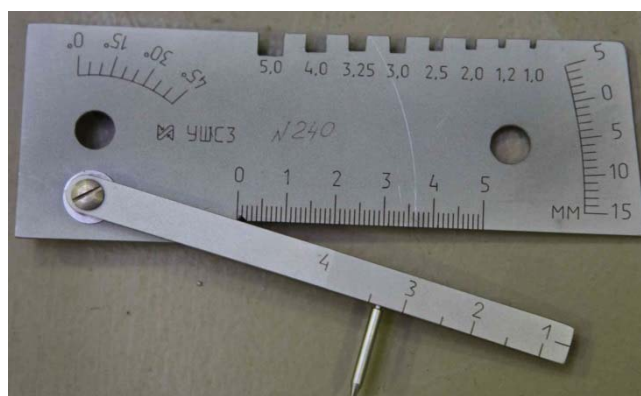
Измерения с помощью шаблона УШС размеров сварного шва:
